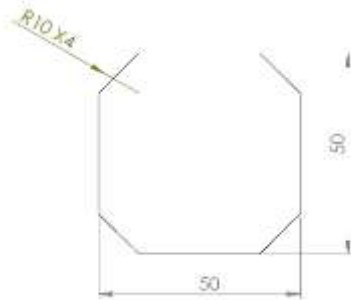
Plano de pieza a fresar mediante función G39. Fuente (El autor).
